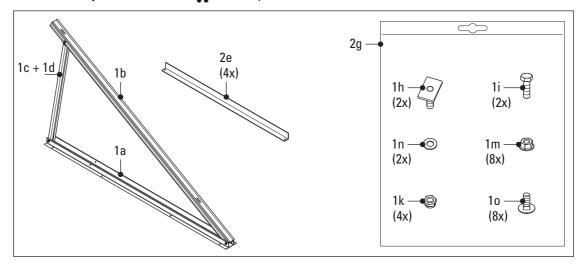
Struttura per tetto piano pacchetto di ampliamento FE V26P
